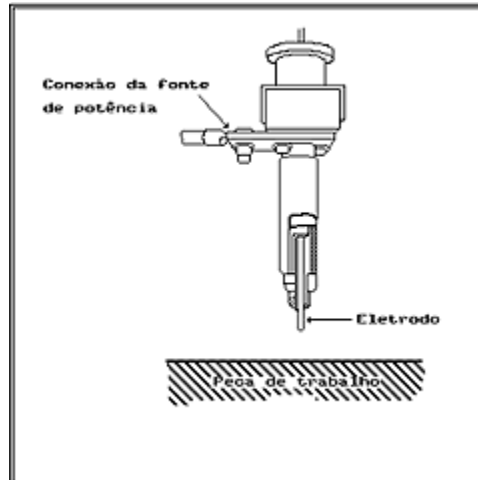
Tocha para soldagem automática sem proteção gasosa
